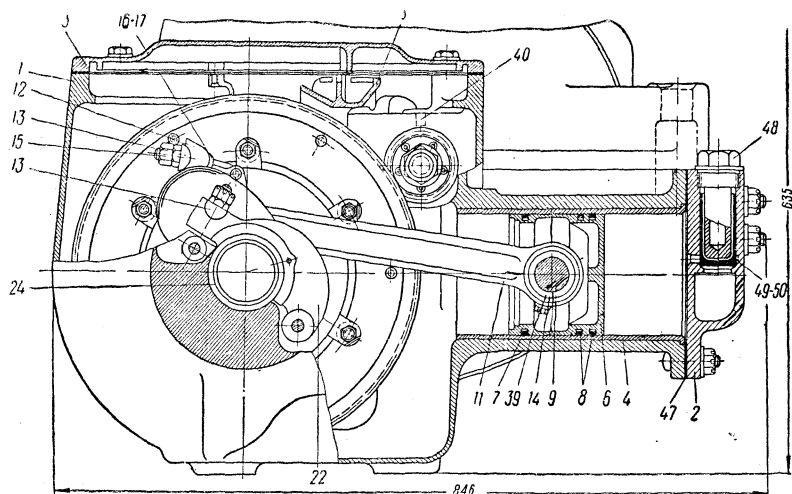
Мотор-компрессор усл. № Э-400 (вид сбоку в разрезе по цилиндрам)
